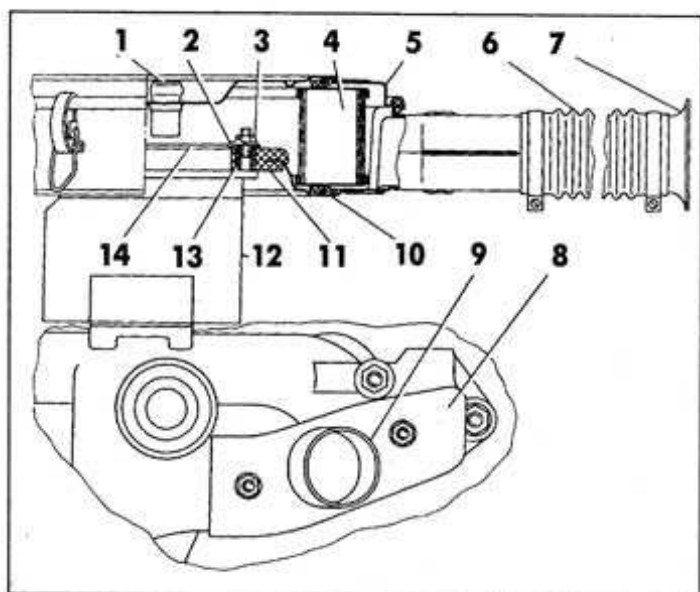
Воздушный фильтр: 1 – патрубок вентиляции картера двигателя; 2 – шайба; 3 – гайка; 4 – фильтрующий элемент; 5 – крышка; 6 – шланг; 7 – заборный патрубок; 8 – экран; 9 – патрубок экрана; 10 – корпус фильтра; 11 – прокладка; 12 – карбюратор; 13 – распорная втулка; 14 – пластина
